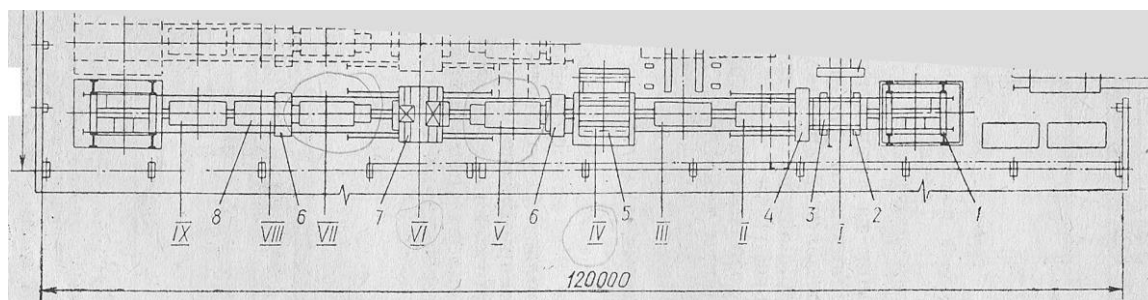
Конвейєрна лінія виготовлення багатопорожнинних плит: 1 — підйомач-знижувач; 2 — обладнання для відкривання і закривання бортів; 3 — машина для обрізування стержнів; 4 — машина для очищення і змазування форм; 5 — установка СМЖ-484; 6 — каретки з порожниноутворювачами; 7 — бетоноукладач; 8 — піддон-візок; 9 — площадка переоснащення і ремонту форм; 10 — конвейєр витримування і вивезення виробів; 11 — знімач-перевантажувач
